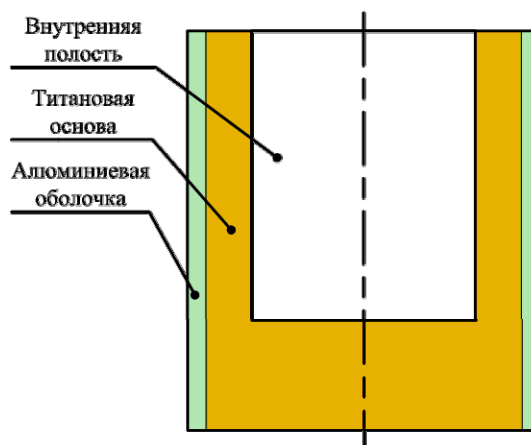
Получение покрытия на боковой поверхности юбки при помощи трубной алюминиевой заготовки
